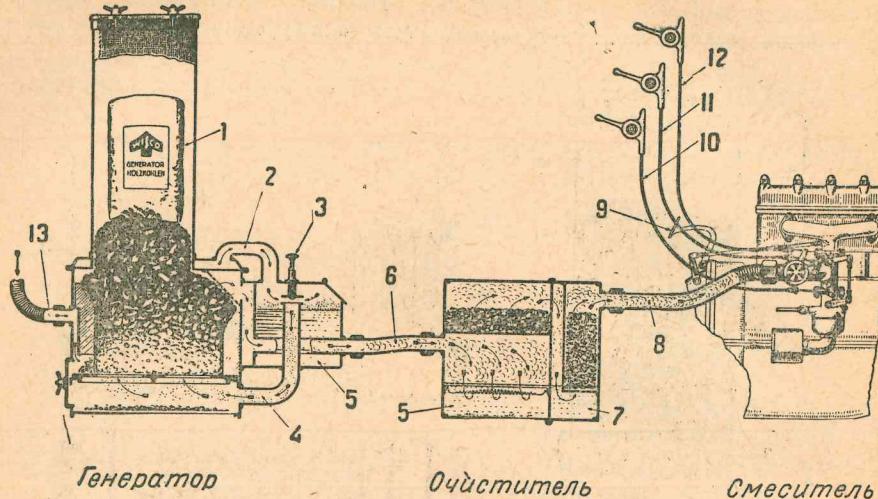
Схема газогенераторной установки Виско-Автогаз: 1—древесный уголь в специальном бумажном мешке; 2—горячий воздух; 3—регулирующий клапан; 4—паровоздушная смесь; 5—вода; 6—подвод газа к очистителю; 7—масло; 8—подвод газа к смесителю; 9—ак елератор; 10—управление дросселем карбюратора; 11—управление дросселем газа; 12—управление дросселем воздуха; 13—питание газогенератора от вентилятора
